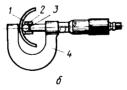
Инструмент и приспособления для измерения толщины тонкостенных вкладышей:
